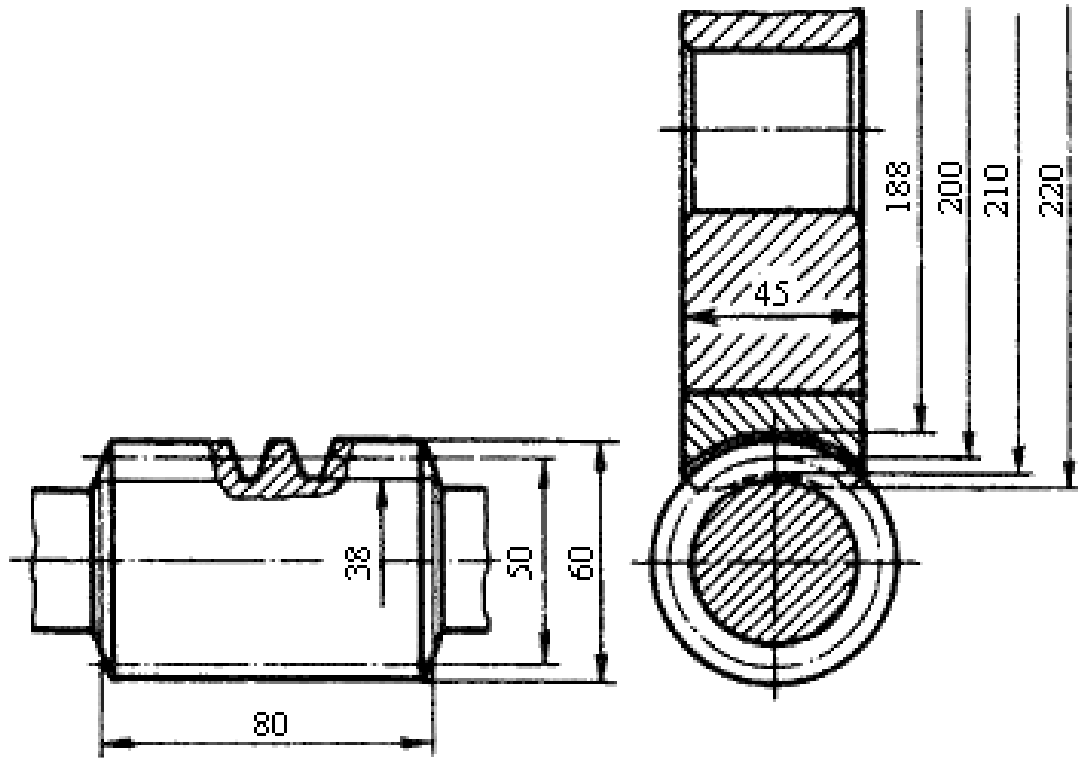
Конструктивна схема черв'яка та черв'ячного колеса
